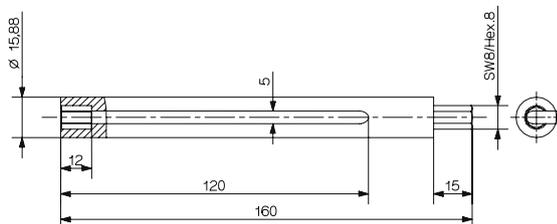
Montageschlüssel für tiefe Bohrungen Typ 1300A41
